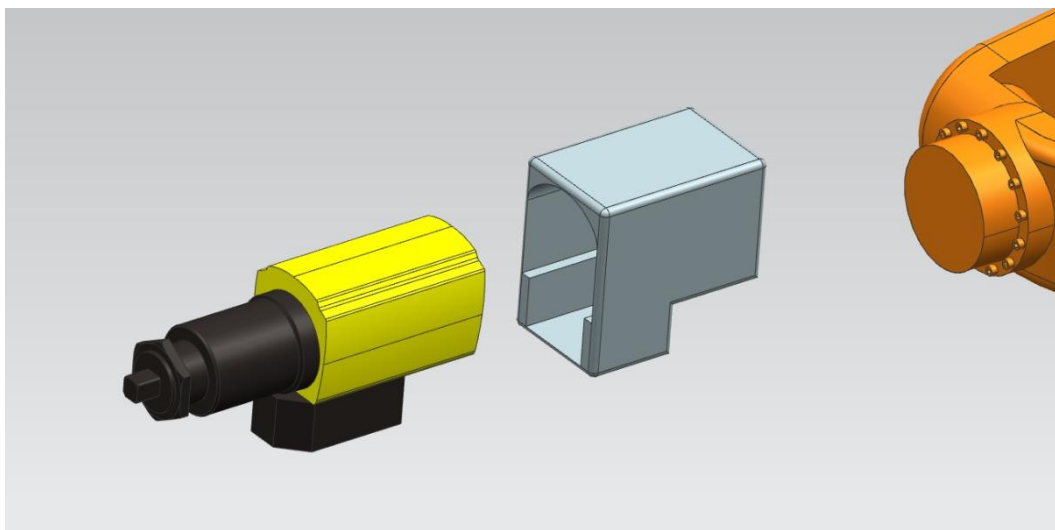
Montaje de la pistola de impacto neumática en el útil acoplable a la brida de montaje
